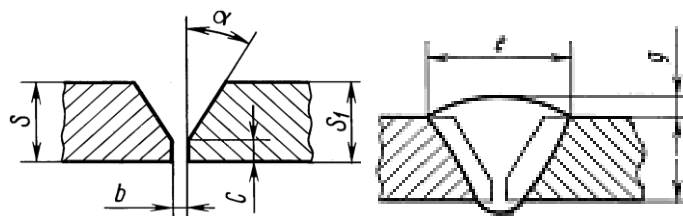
Форма разделки кромок и параметры сварного шва
